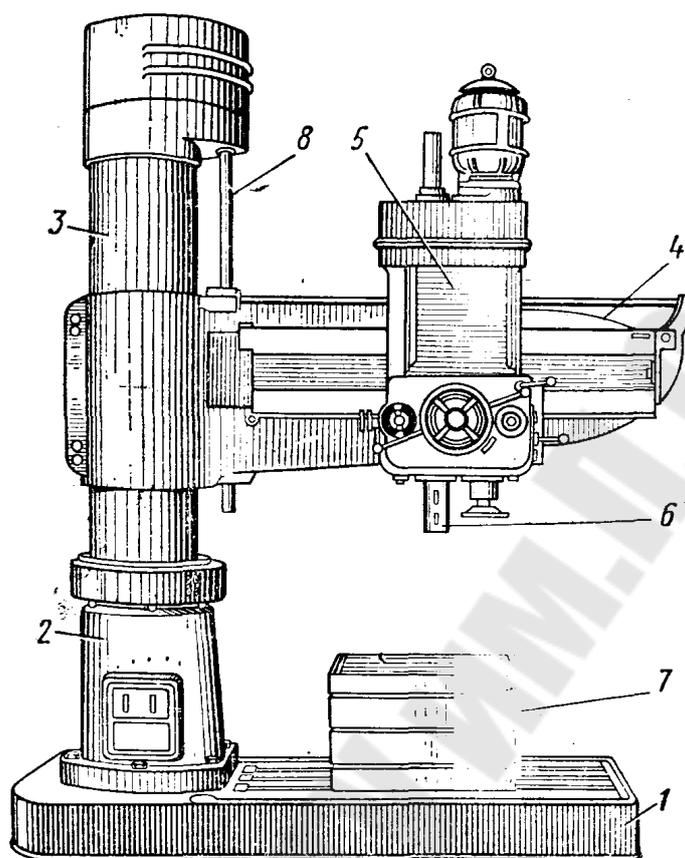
Общий вид радиально-сверлильного станка
